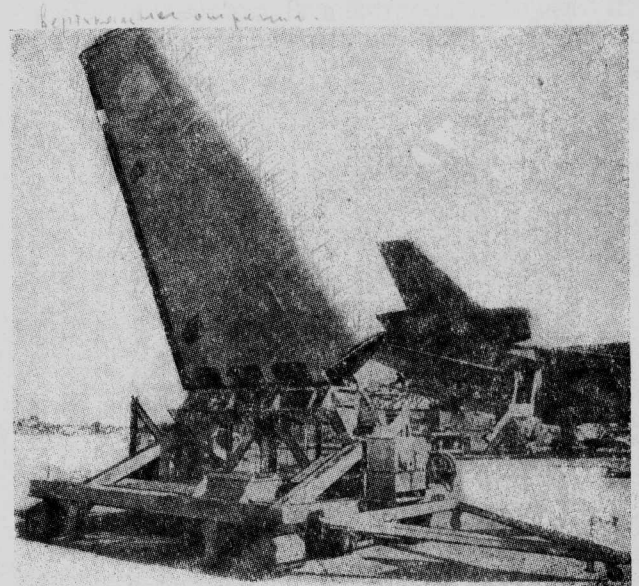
Опытный образец кия самолета DC-10, изготовленный из КМ
